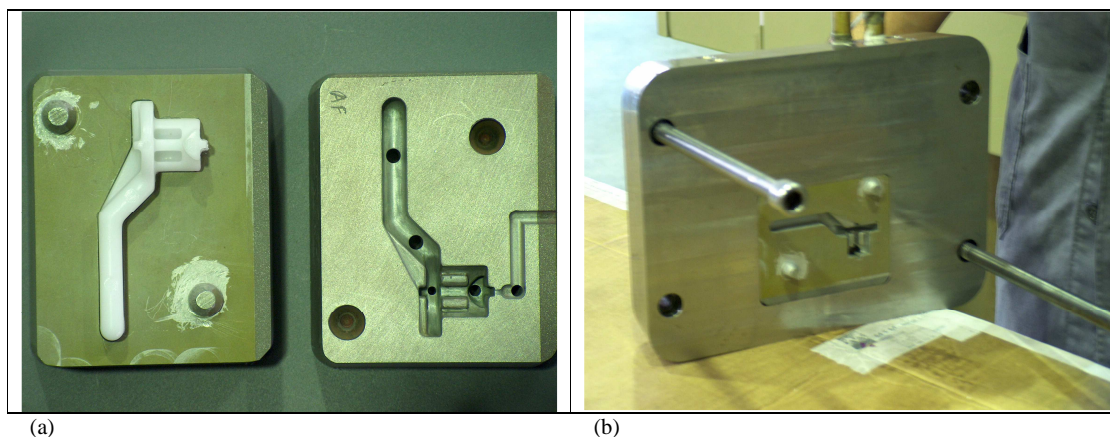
(a) peça injectada, cavidade e bucha em resina, sendo nesta última visível o gito de enchimento e os furos dos extractores; (b) placa porta-insertos contendo o molde rápido de resina (cavidade) para ser testado.
